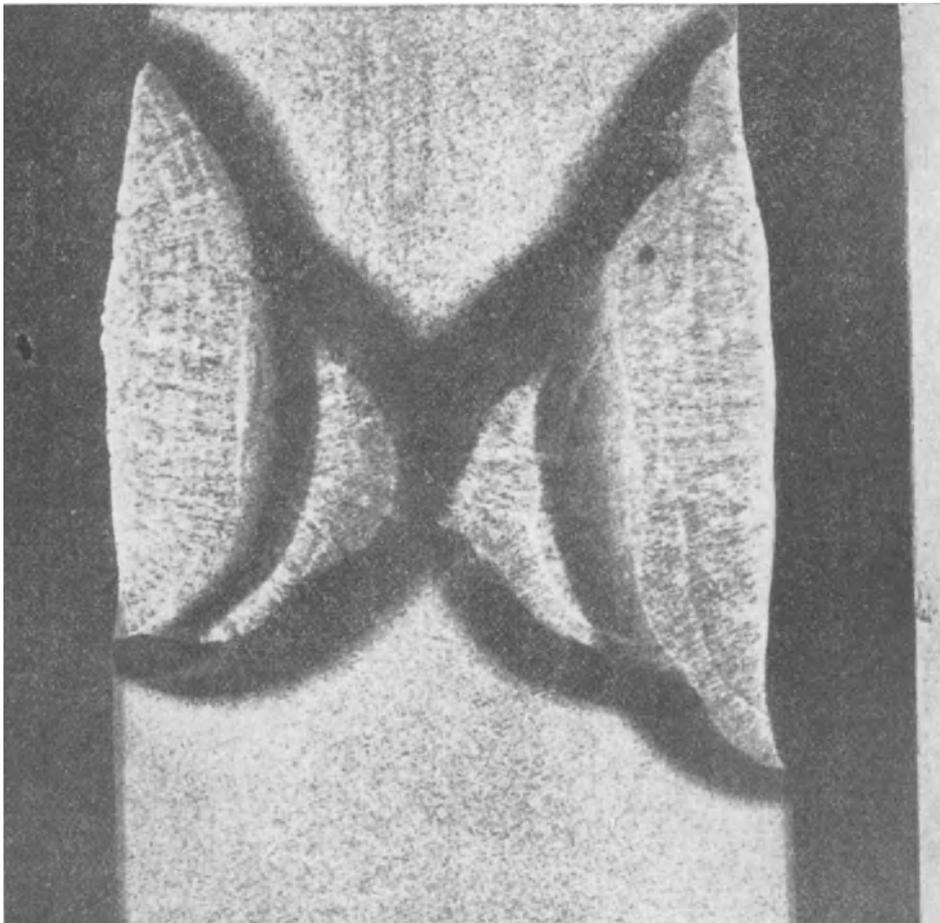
Querschnitt einer Schweißnaht mit gehärteten Übergangszonen.
